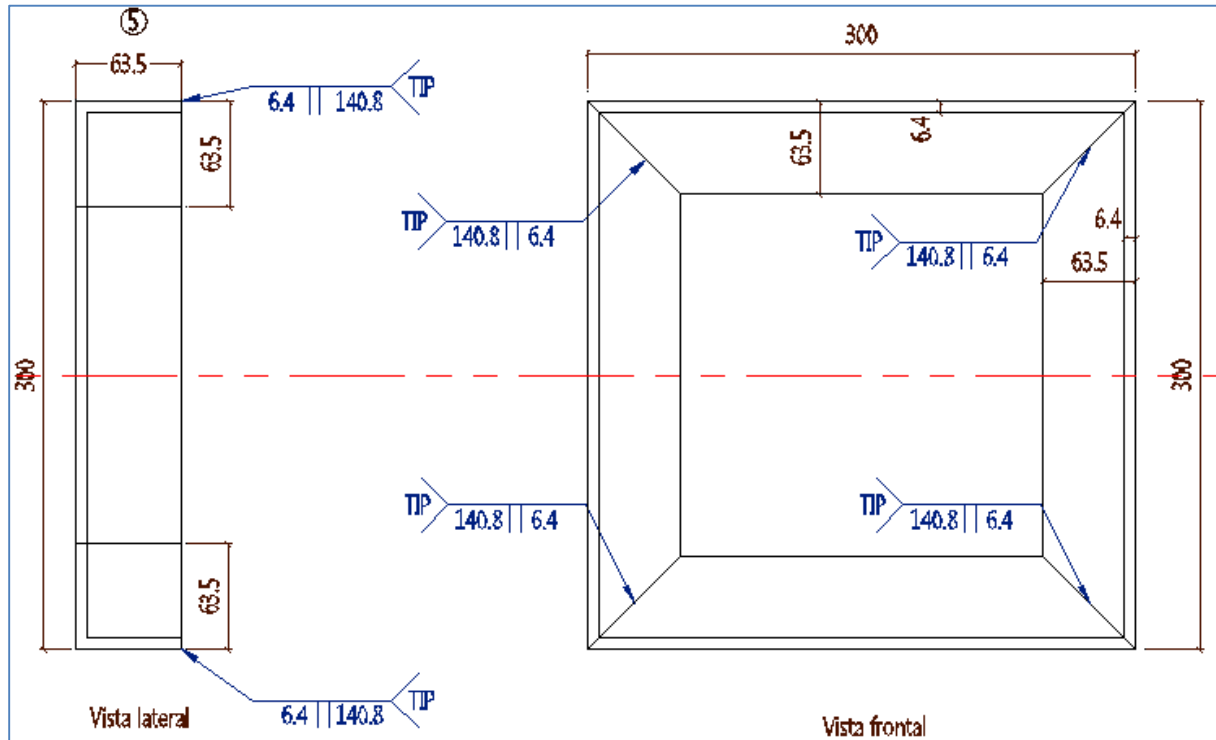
Detalle despiece pieza No.5 modelo 1 corte.
